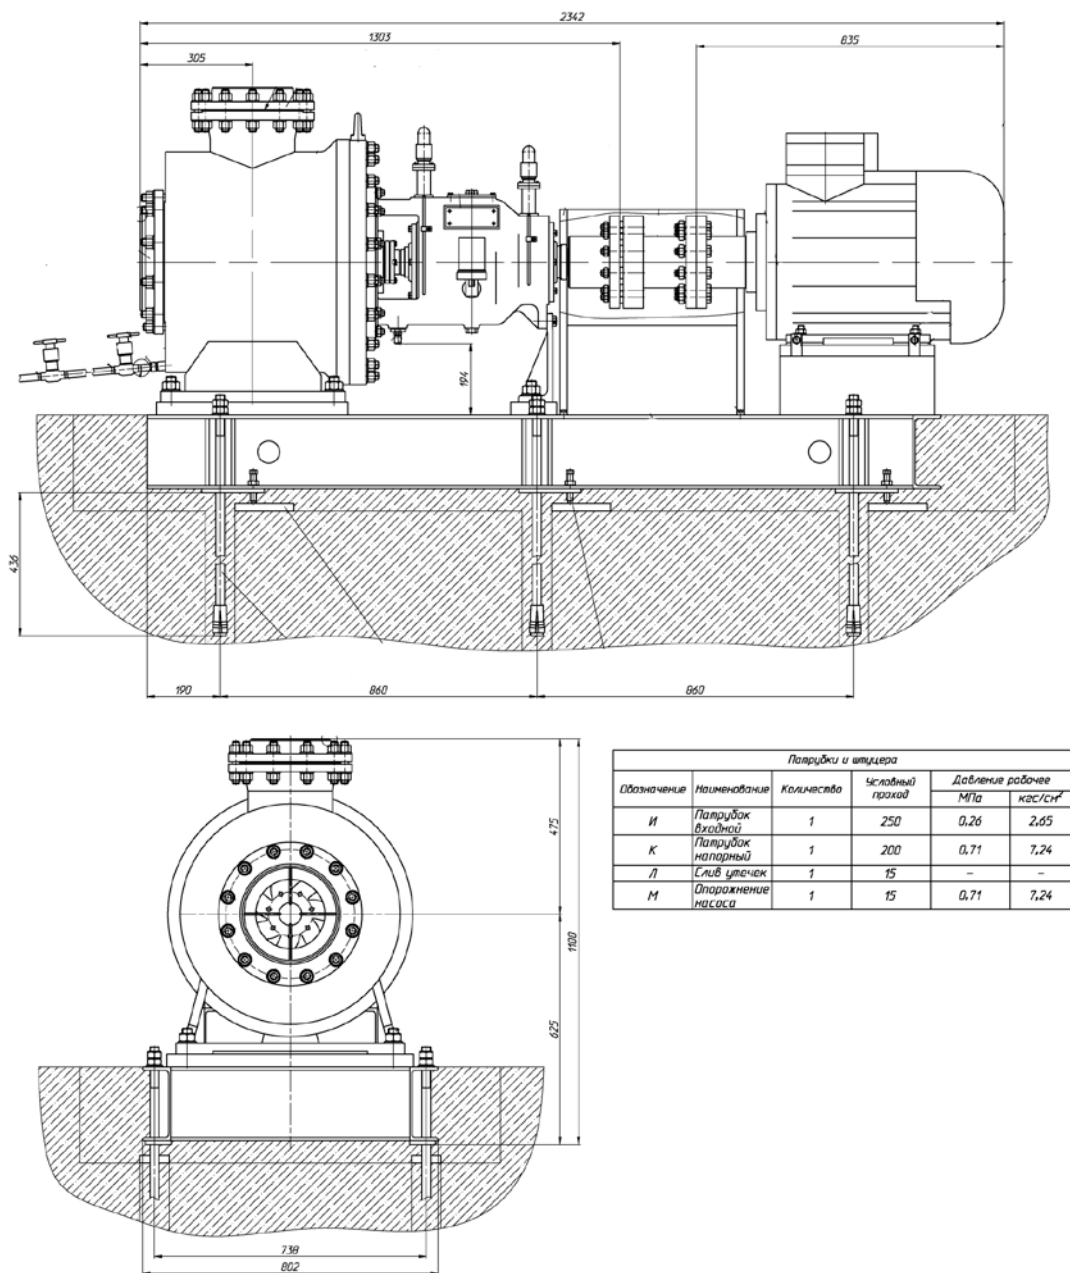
Габаритный чертеж агрегата электронасосного типа ЦНА 400/30
